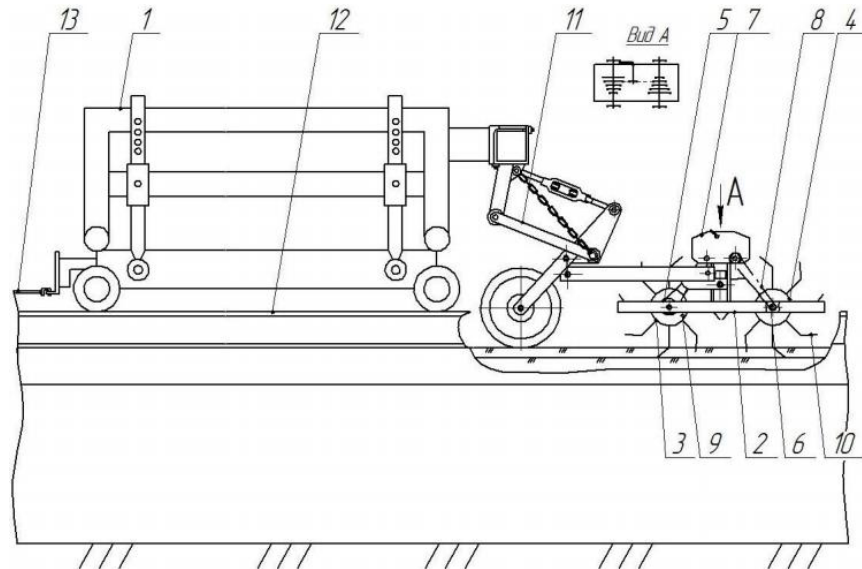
Схема випробувань лабораторної установки в ґрунтовому каналі кафедри: 1 – приводний візок; 2 – рама; 3 – передній ротор; 4 – задній ротор; 5 – зірочка переднього ротора; 6 – зірочка заднього ротора; 7 – ланцюговий редуктор; 8 – ланцюг; 9 – диск; 10 – ніж; 11 – паралелограмний механізм; 12 – рейки; 13 – трос.
